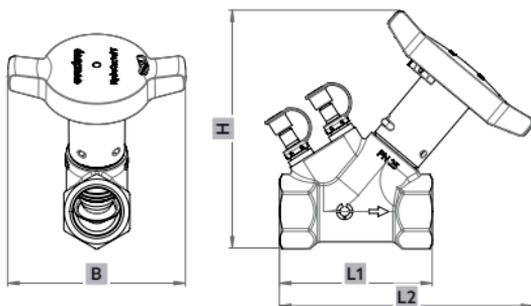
Abmessungen Seitenansicht / Frontansicht Innengewinde
